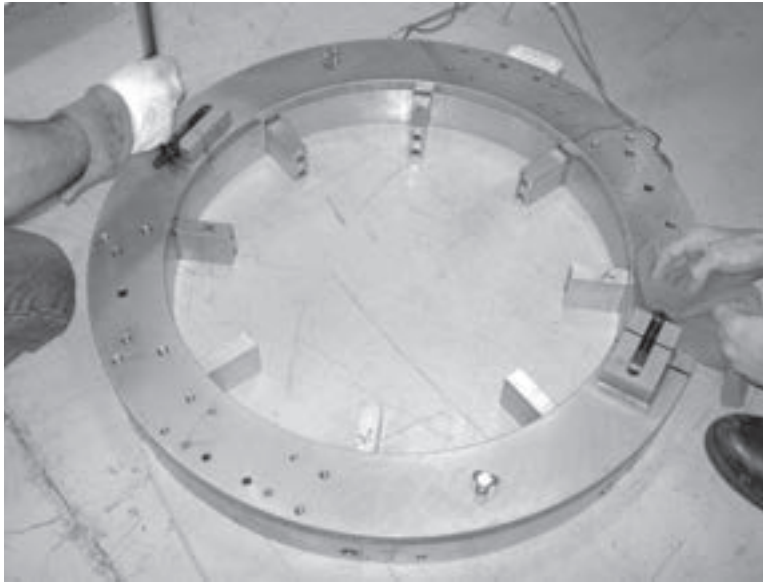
Ensamble la máquina en el suelo para usarla en un tubo de extremo abierto.
